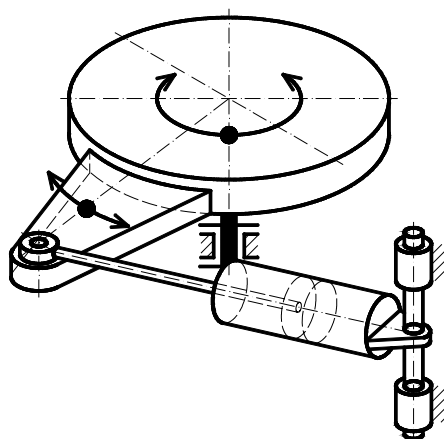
Rotační motor – kývavý pohyb
